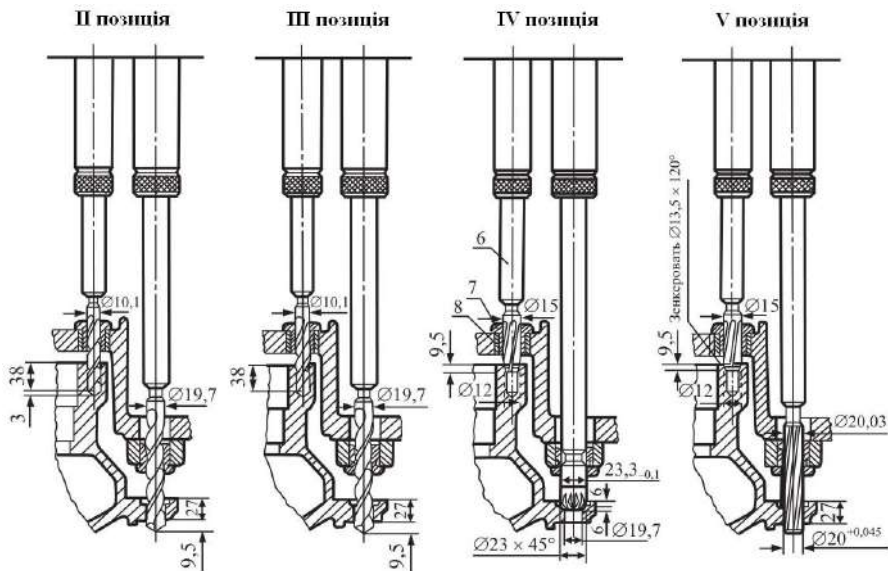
Обробка корпусів підшипників на п'ятипозиційному вертикальному агрегатному верстаті
